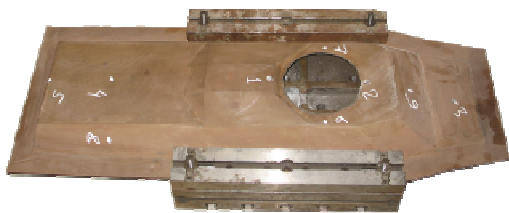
Макет фрагменту корпусу БТР-80 із заданими місцями кріплення датчика
